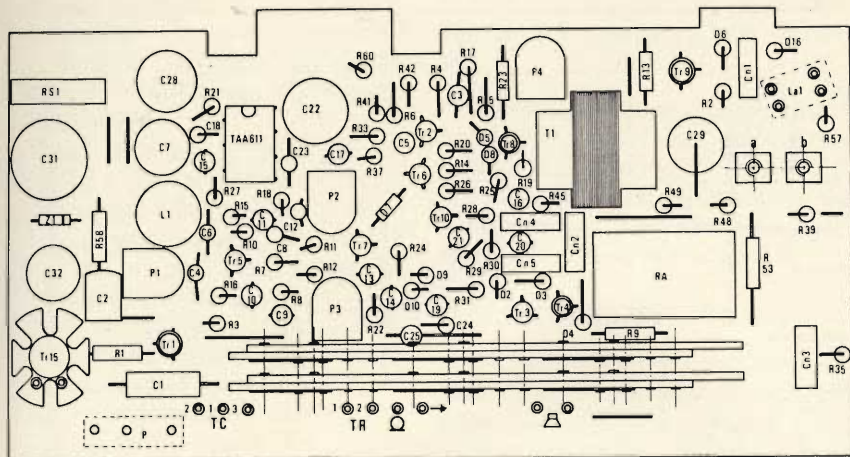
Circuito stampato del SENTAPHON T3 visto dal lato componenti.
